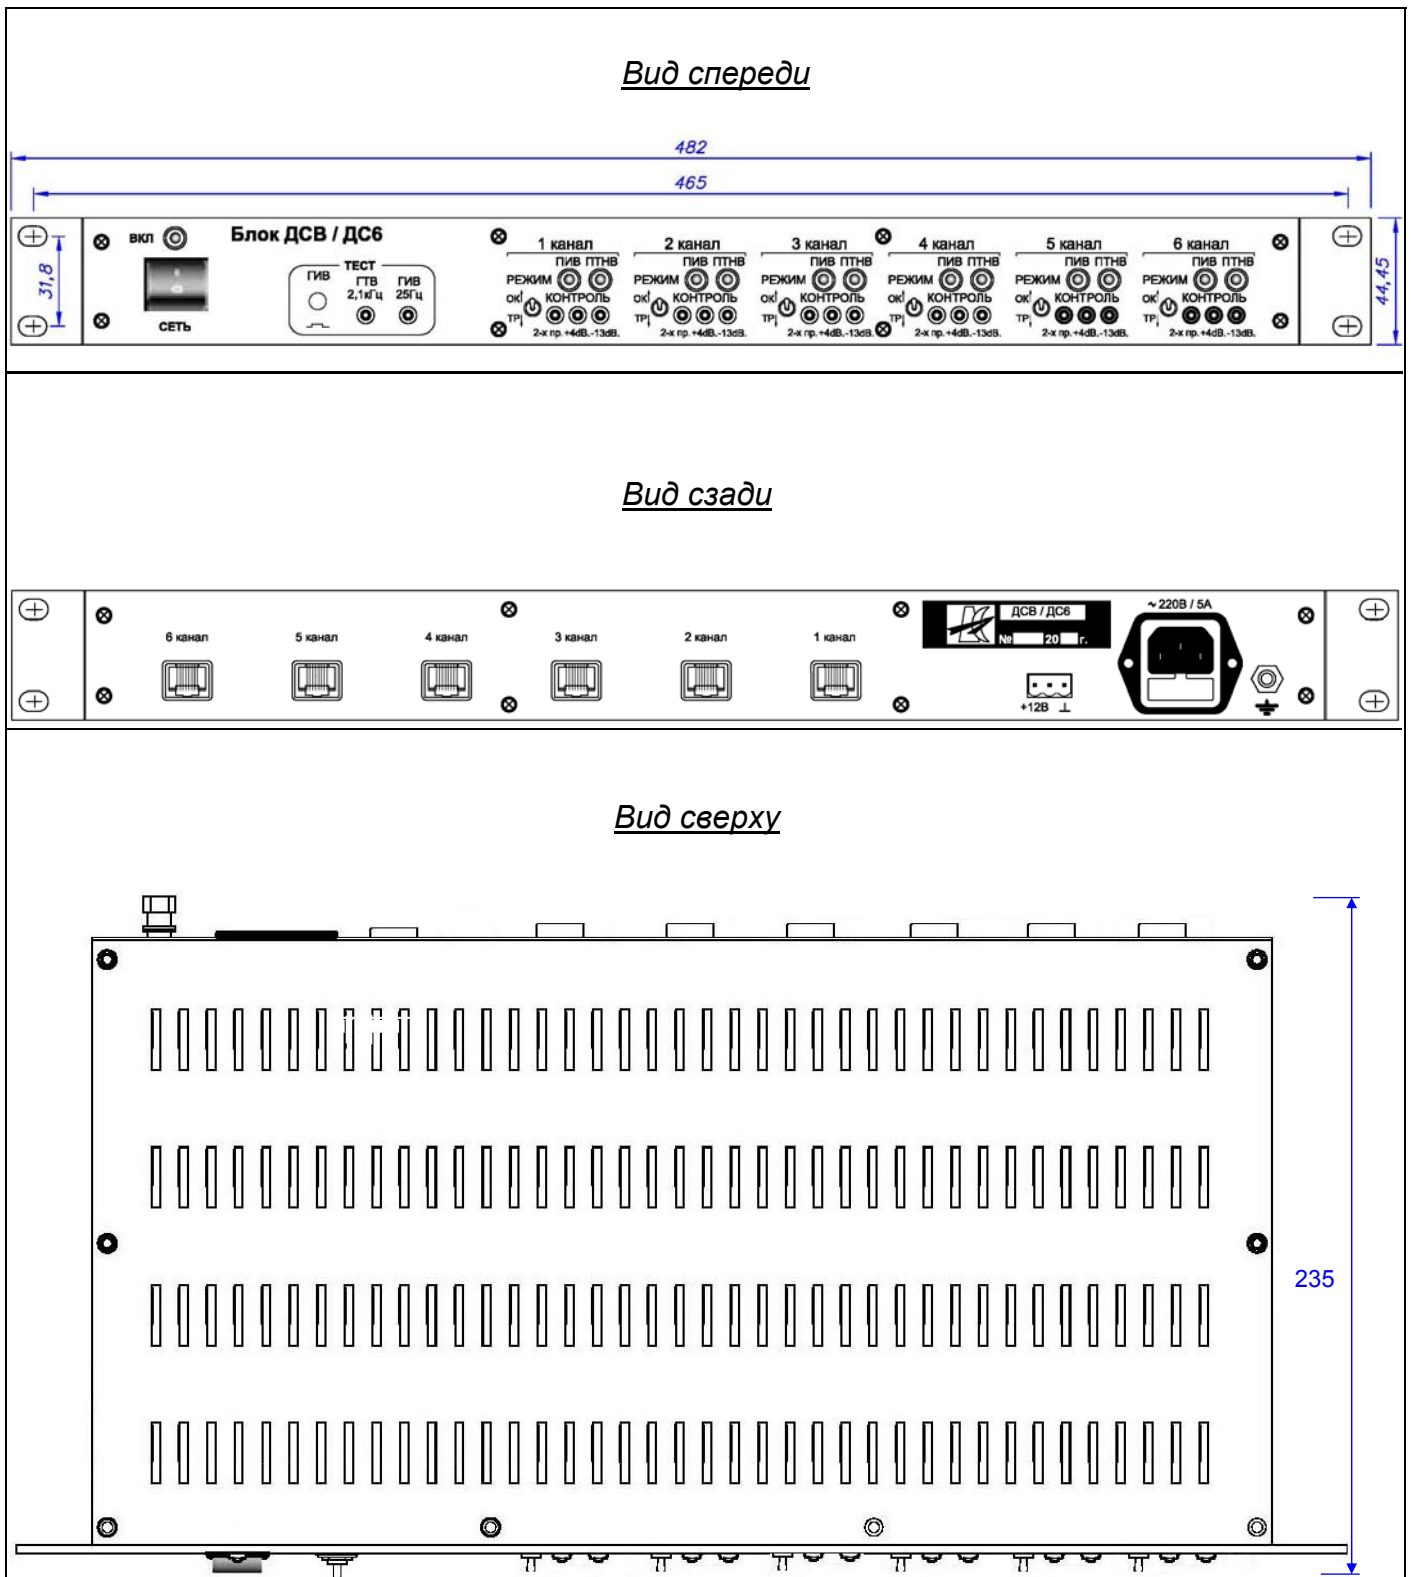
Внешний вид и габаритные размеры блока ДСВ / ДС6.
